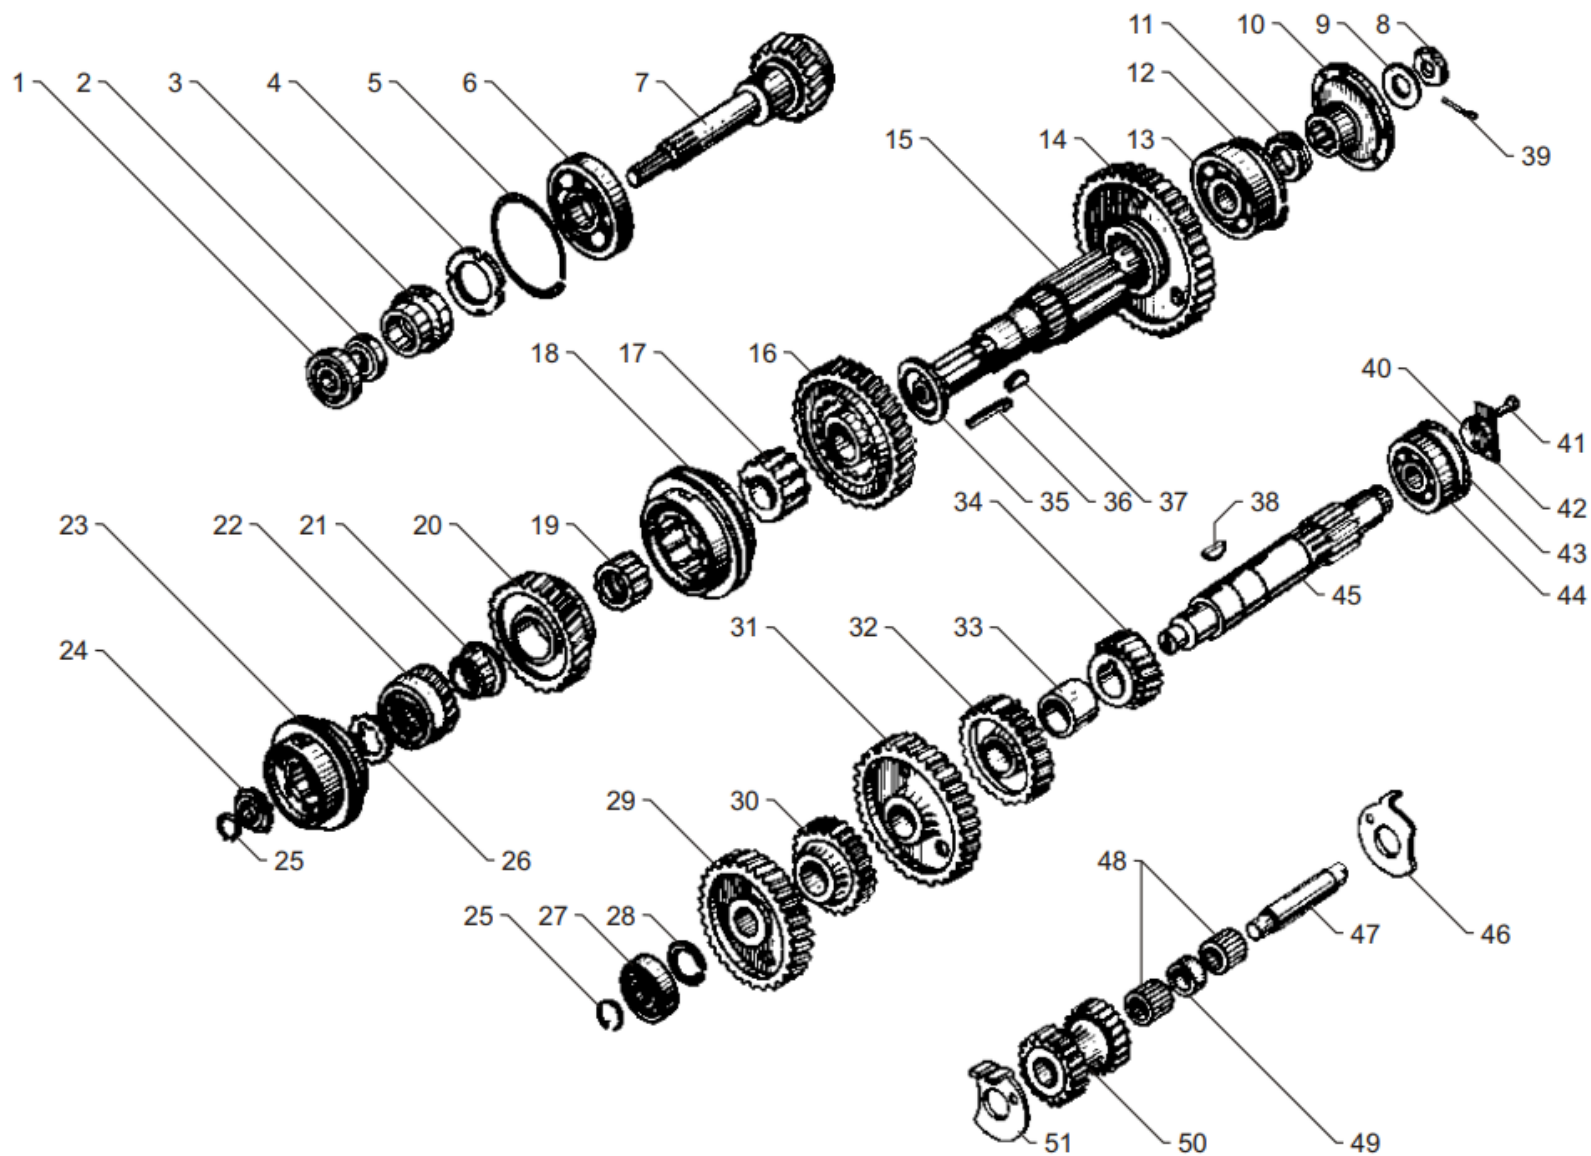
ВАЛЫ И ШЕСТЕРНИ КОРОБОК ПЕРЕДАЧ ЯМЗ-236Н И ЯМЗ-236П
